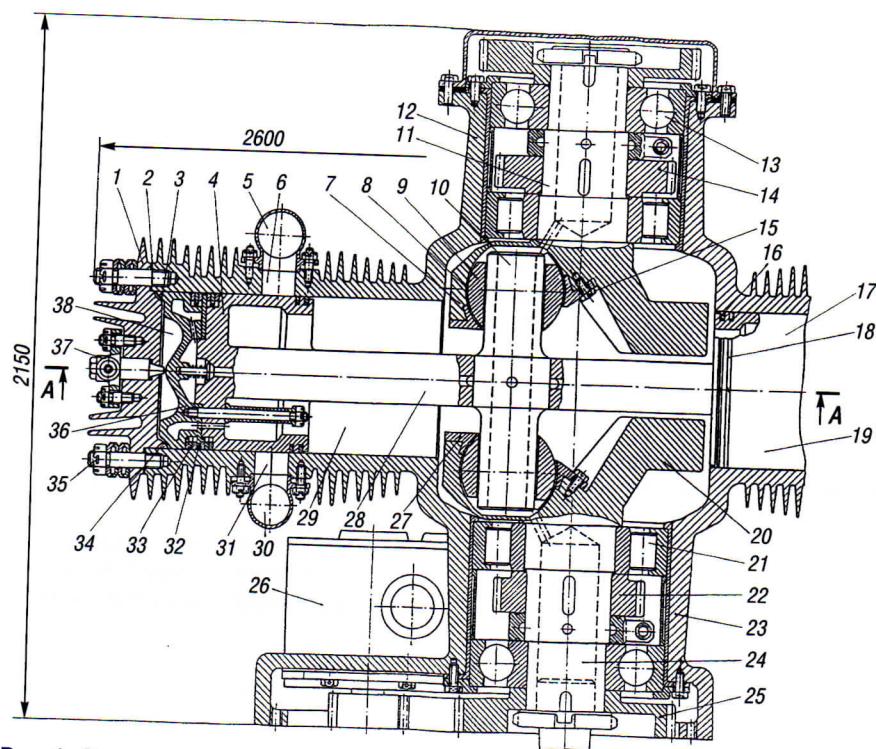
Эскизный проект двухтактного дизеля с двухкристошипным приводным механизмом:
